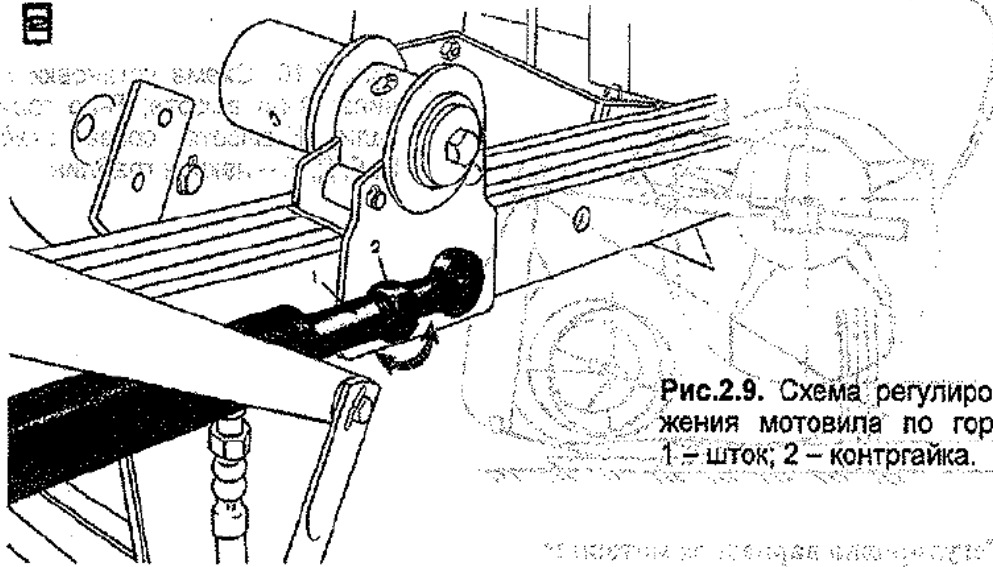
Схема регулировки положения мотовила по горизонтали: 1 – шток; 2 – контргайка.
